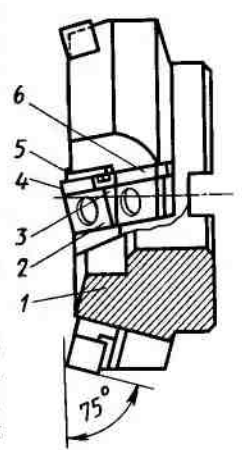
Торцовая фреза с механическим креплением режущих пластин из твердого сплава
